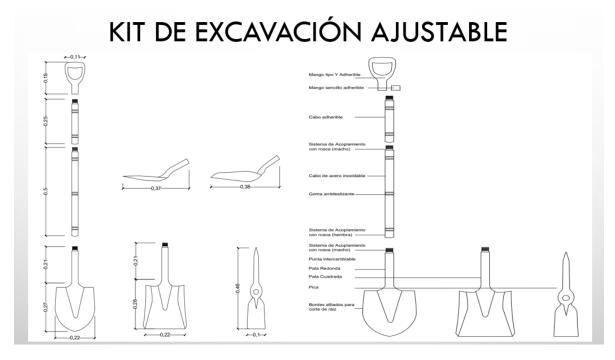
kit de excavación ajustable. 2022 Fuente. Barreto, Sebastián.
